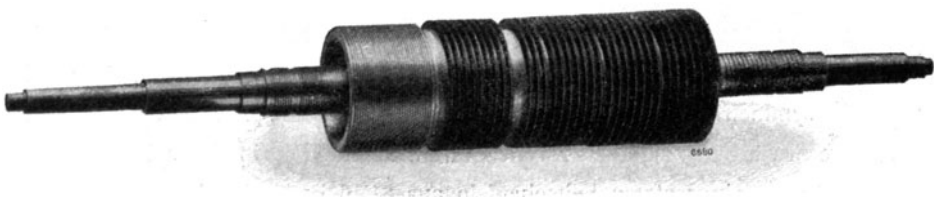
Laufspindel einer Parsons-Gegendruck-Turbine.
